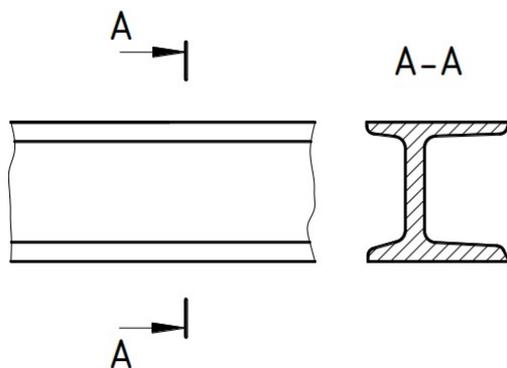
Расположение вынесенного сечения на свободном месте поля чертежа
